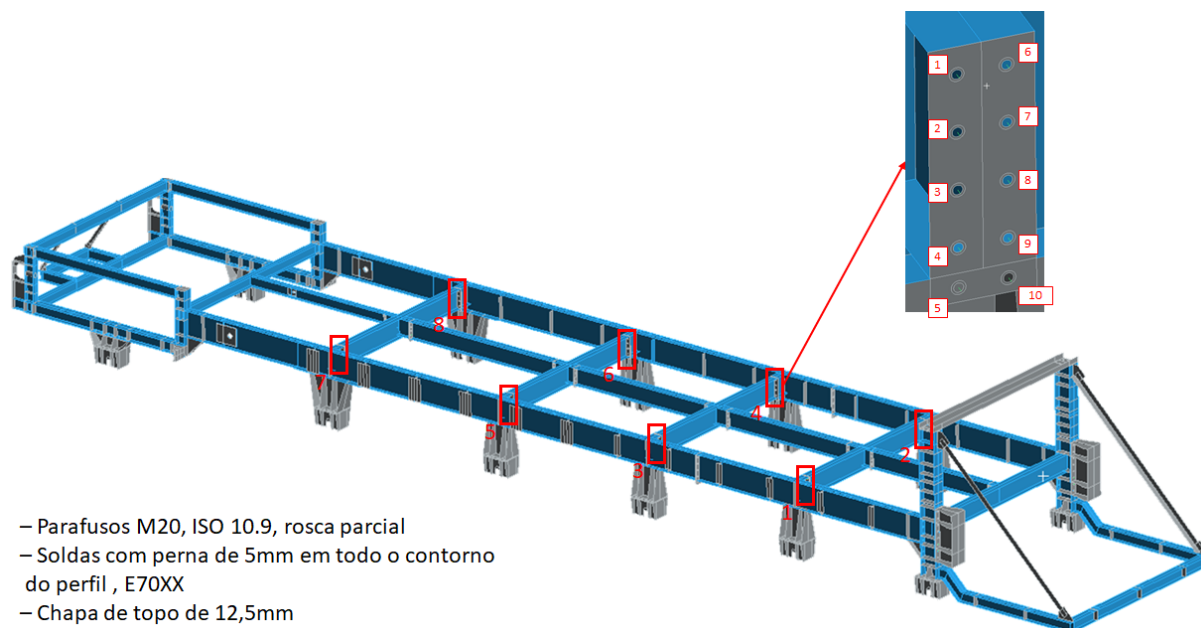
Ligação do chassi XI – Ligação entre a viga transversal e a viga longitudinal principal.
